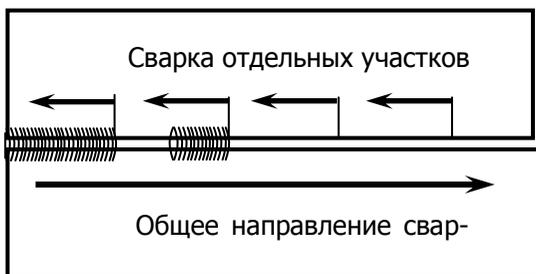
Схема обратноступенчатого способа сварки
